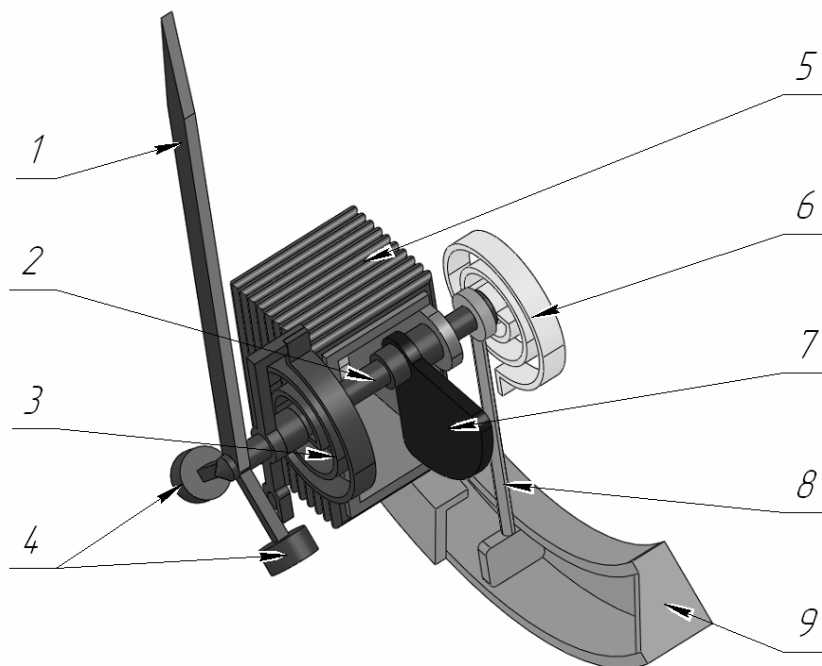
конструкция электромагнитной измерительной системы: 1 – стрелка; 2 – вал (ось); 3 – механизм настройки; 4 – противовес; 5 – катушка; 6 – спиральная пружина; 7 – ферромагнитный сердечник; 8 – шток; 9 – цилиндр
